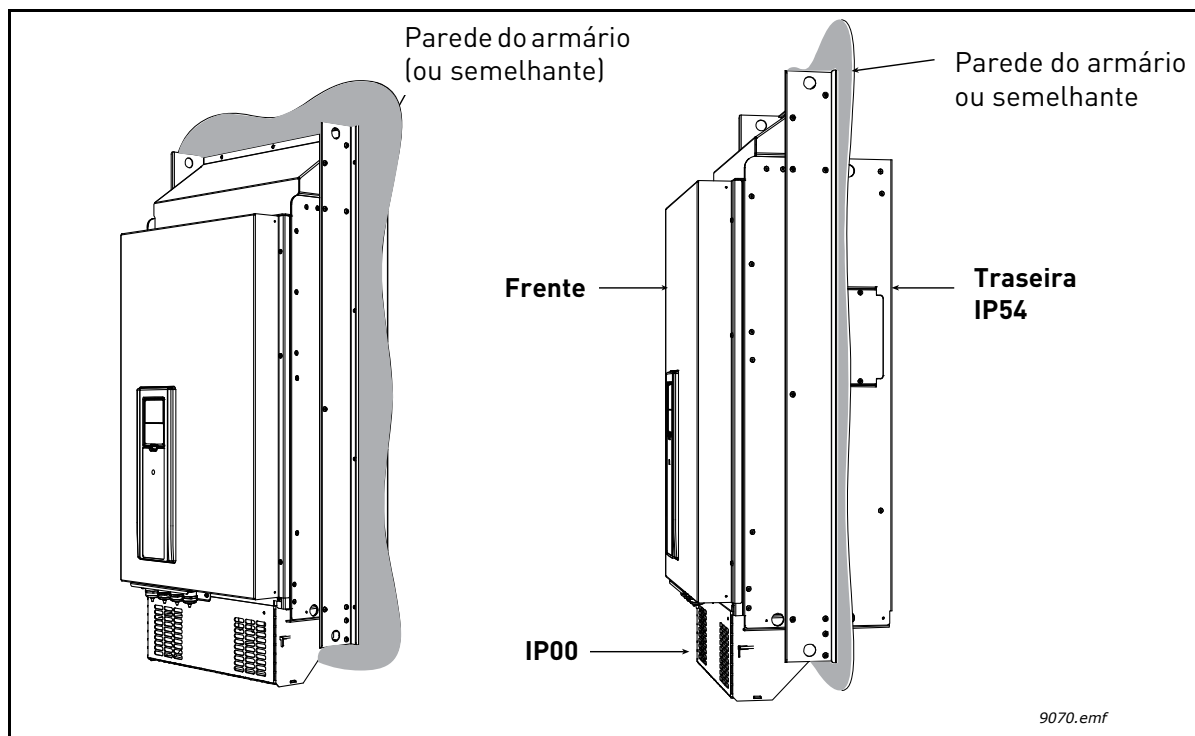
Exemplo de montagem com flange (estrutura MR9)
